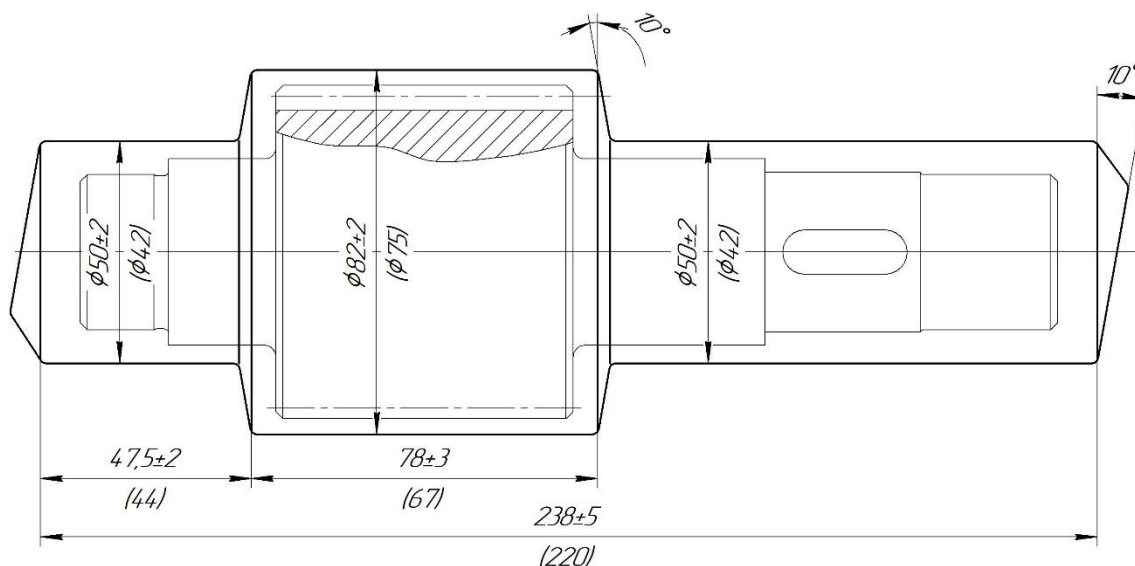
Приклади виконання ескіза кованої заготовки
